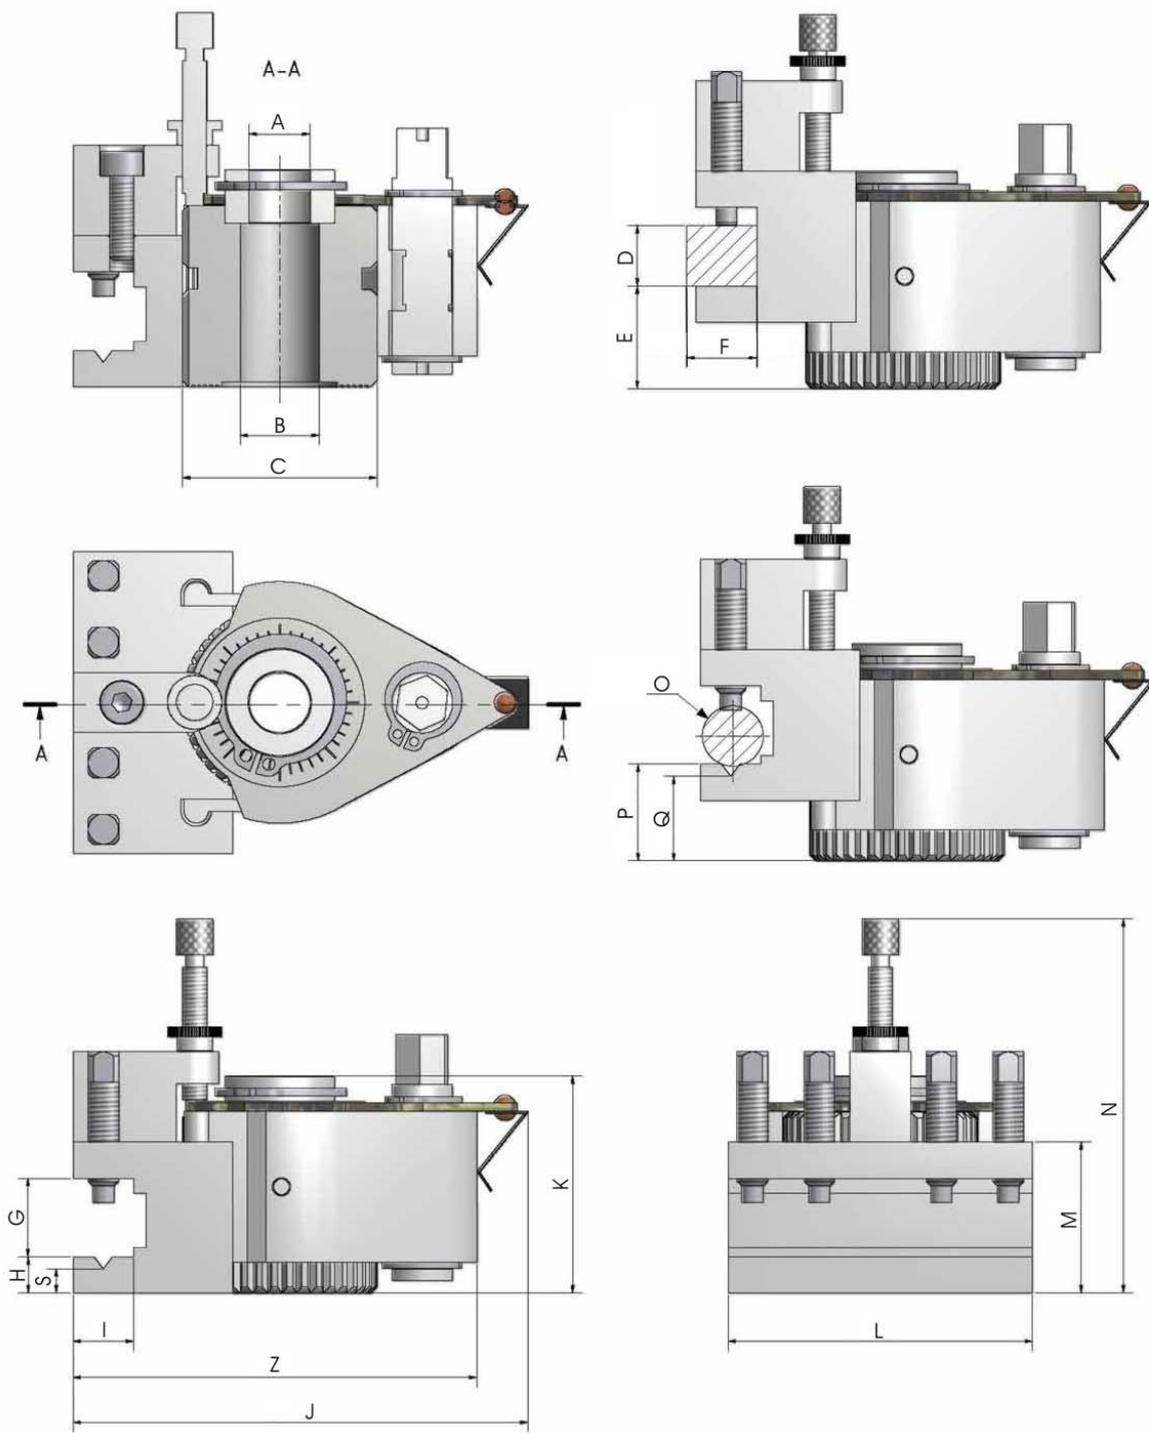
Stahlhalter für Vierkantmeißel/ Rundmeißel
